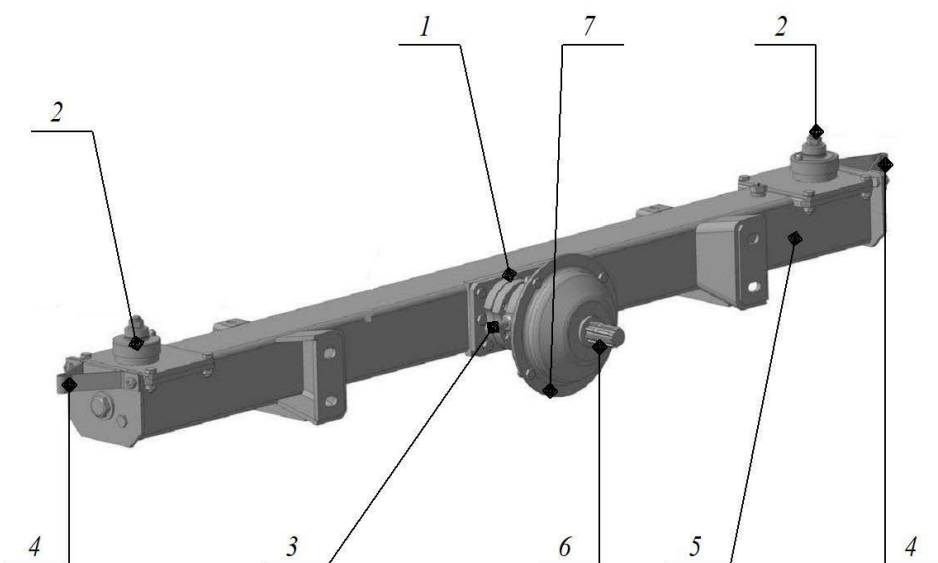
Привод с фрикционной муфтой: 1 – редуктор конический; 2 – конический концевой редуктор; 3 – привод рыхлителя; 4 – элемент для крепления отражателя; 5 – корпус; 6 – вал приема мощности; 7 – фрикционная муфта
